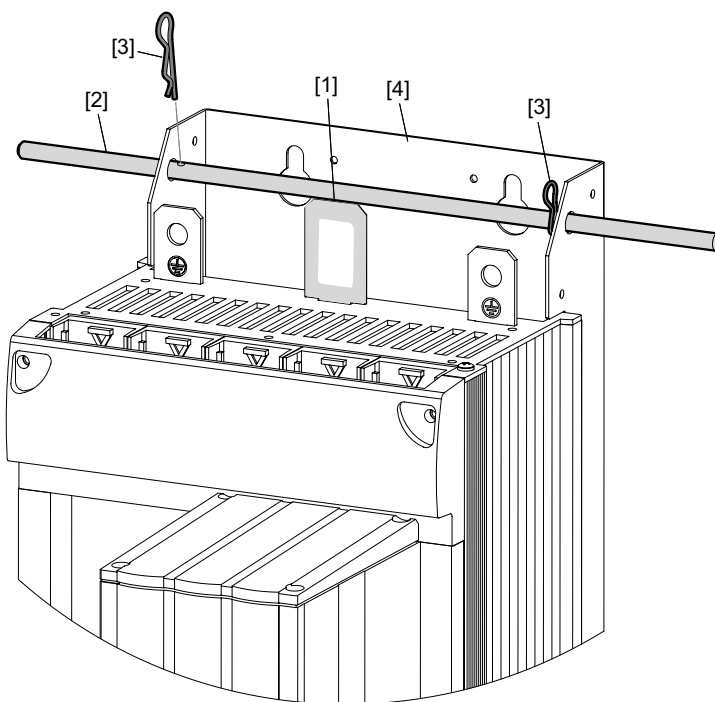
Подъемная проушина и пруток для переноски MOVIDRIVE® типоразмера 6
